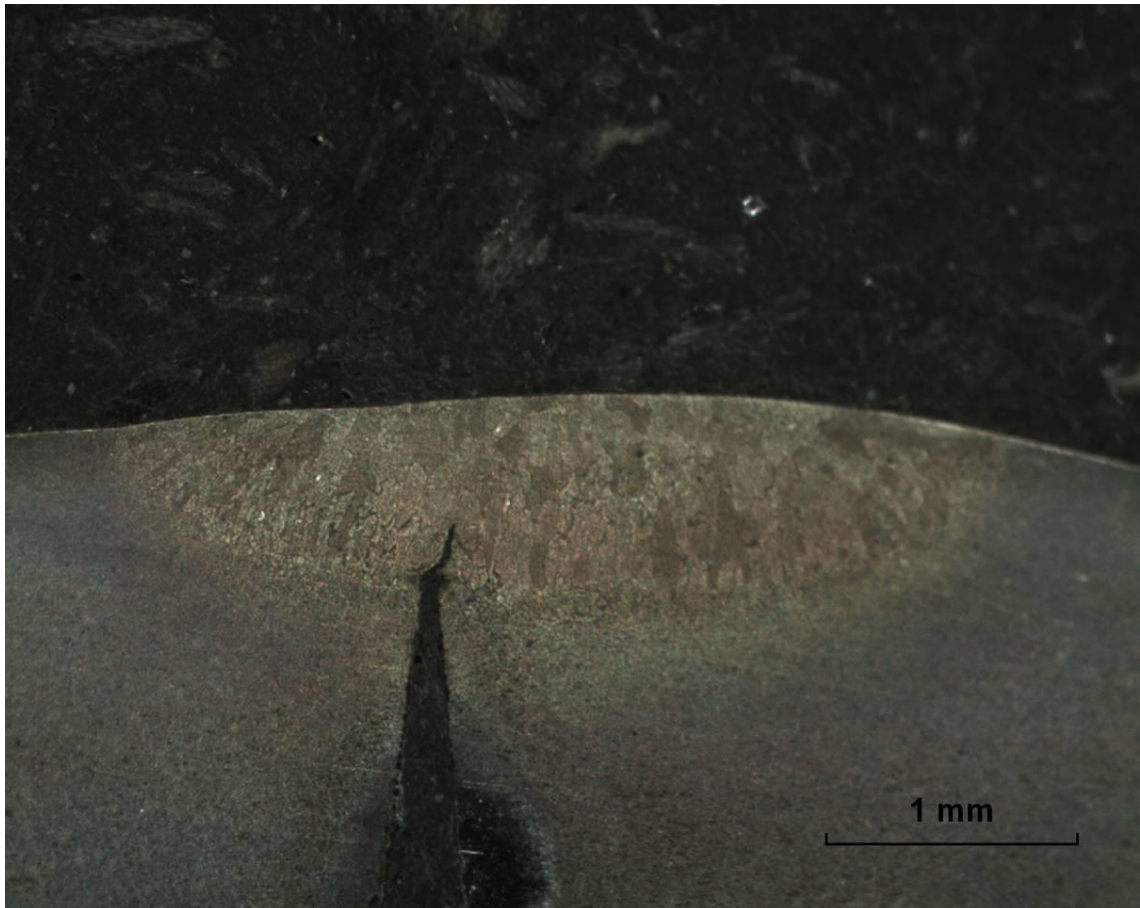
Macrografia da junta soldada arco pulsado. Ampliação 30X; Ataque: Behara.
